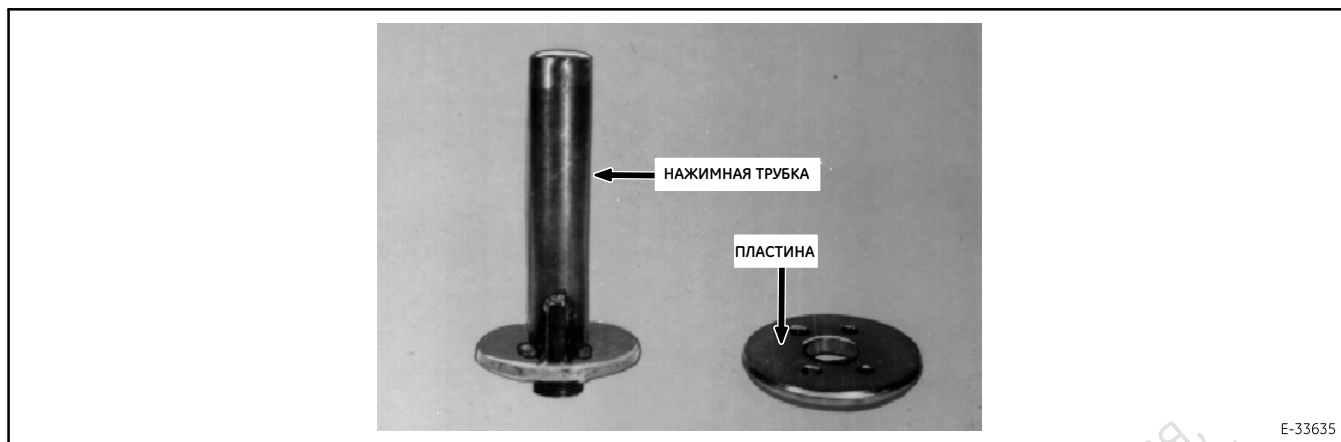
Инструменты для выпрессовки износного кольца из упорного.
